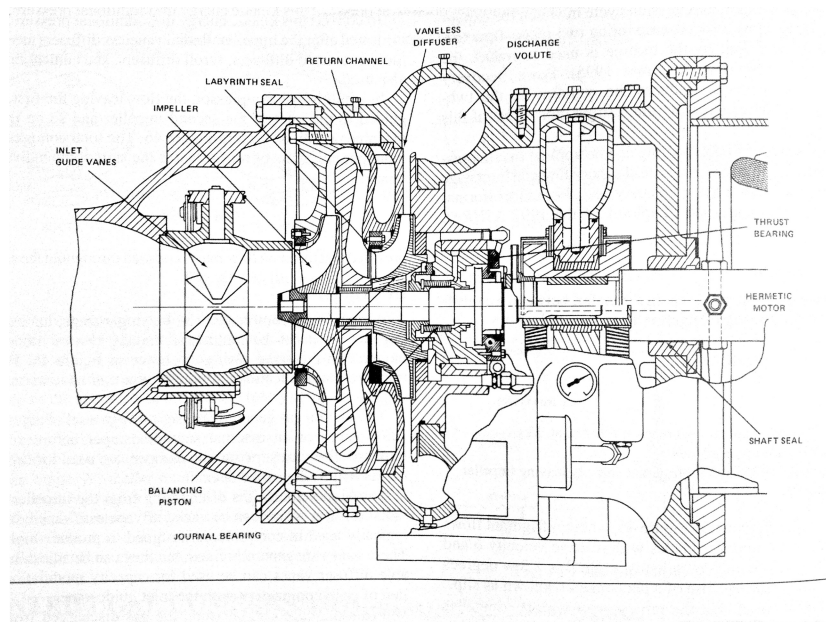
Sezione di un compressore centrifugo per macchina frigorifera, [9, Chapter 4].
